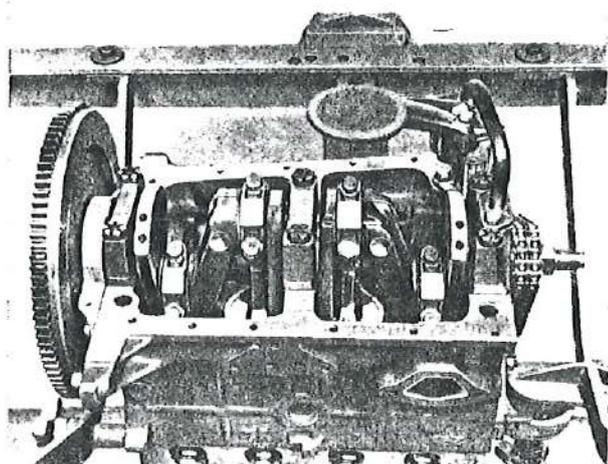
Motor sobre caballete rotativo para la revisión, visto desde la parte inferior del bloque.
